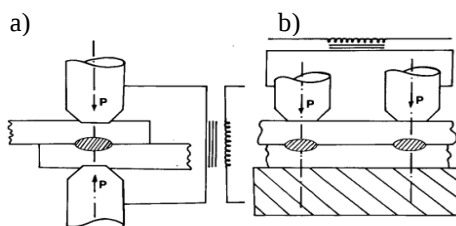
Esquema de soldagem por resistência, (a) solda ponto; (b) solda ponto múltipla.
